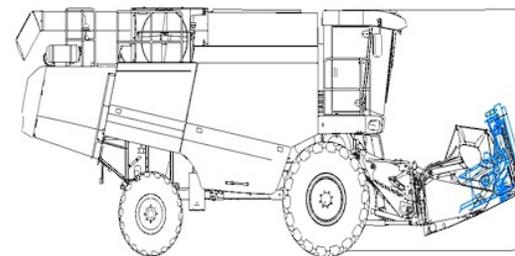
Гидролинии жатки зерновой и приспособления для уборки рапса в комбайне
